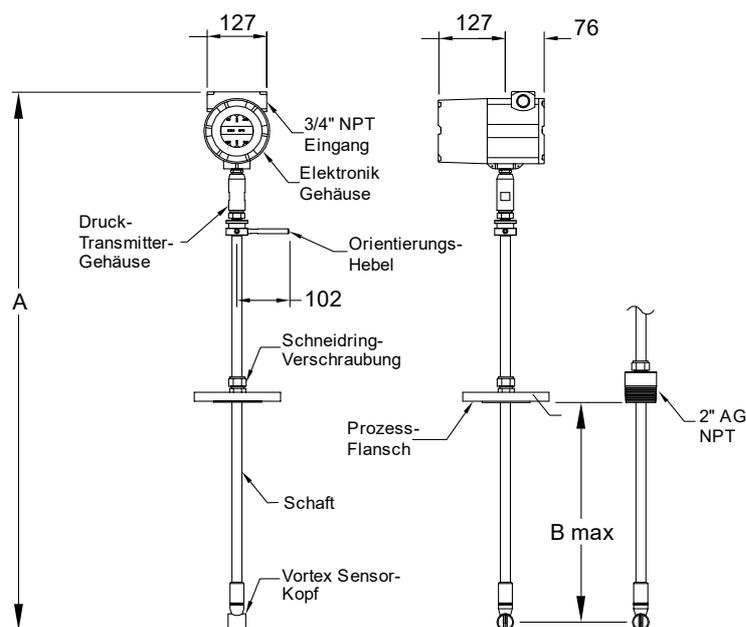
DVE Eintauchversion mit Schneidringverschraubung
